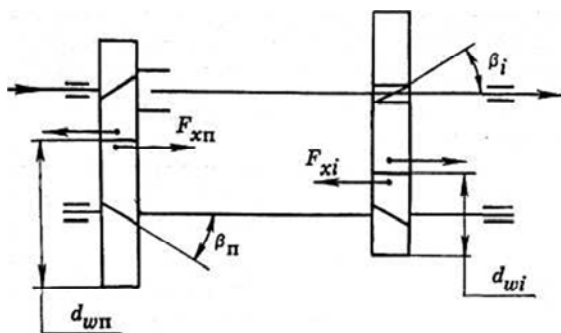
Направление осевых усилий в косозубых колесах трехвальной соосной коробки передач
